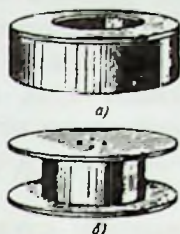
Кассеты для сварочной проволоки:
